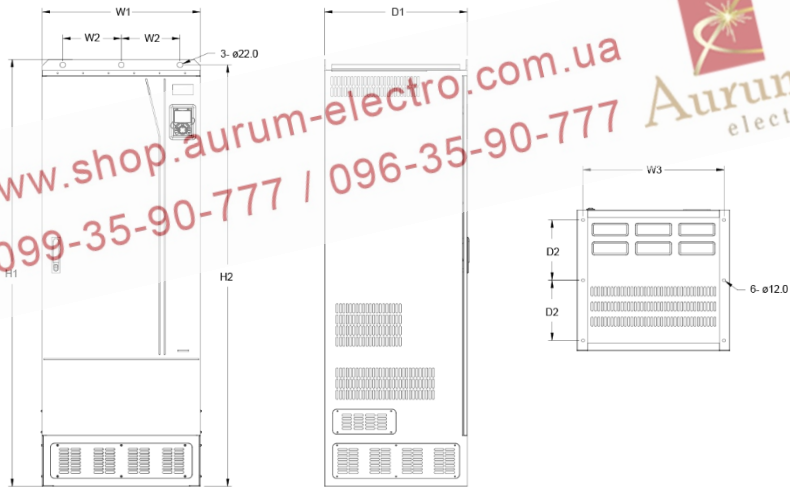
Схема для підлогового монтажу ПЧ напругою 660 В, потужністю від 400 до 630 кВт
